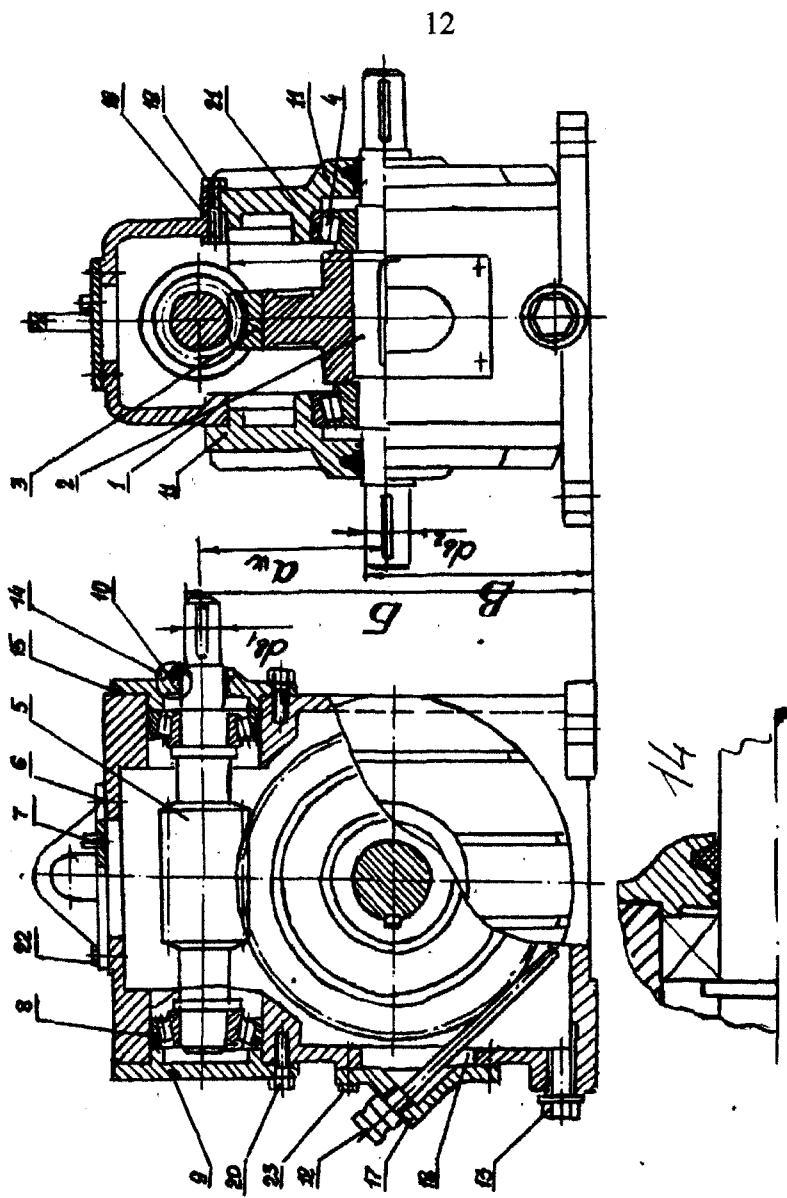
Червячный редуктор с верхним расположением червяка и неразъёмным корпусом
